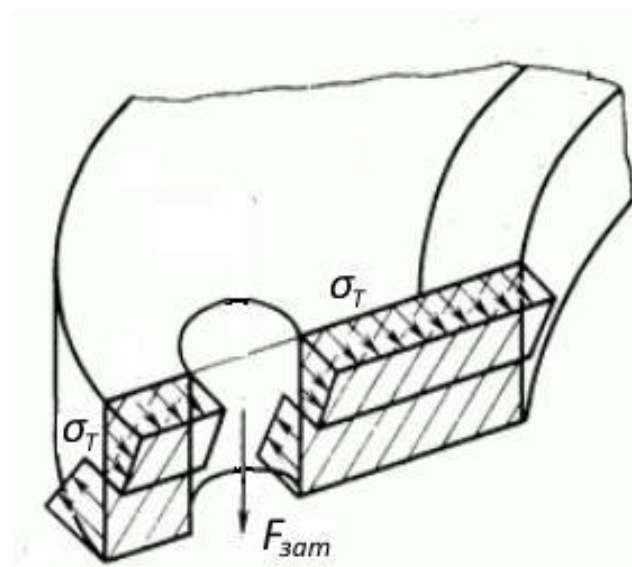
Уточняющая расчётная схема фланцевого соединения крышки с корпусом
